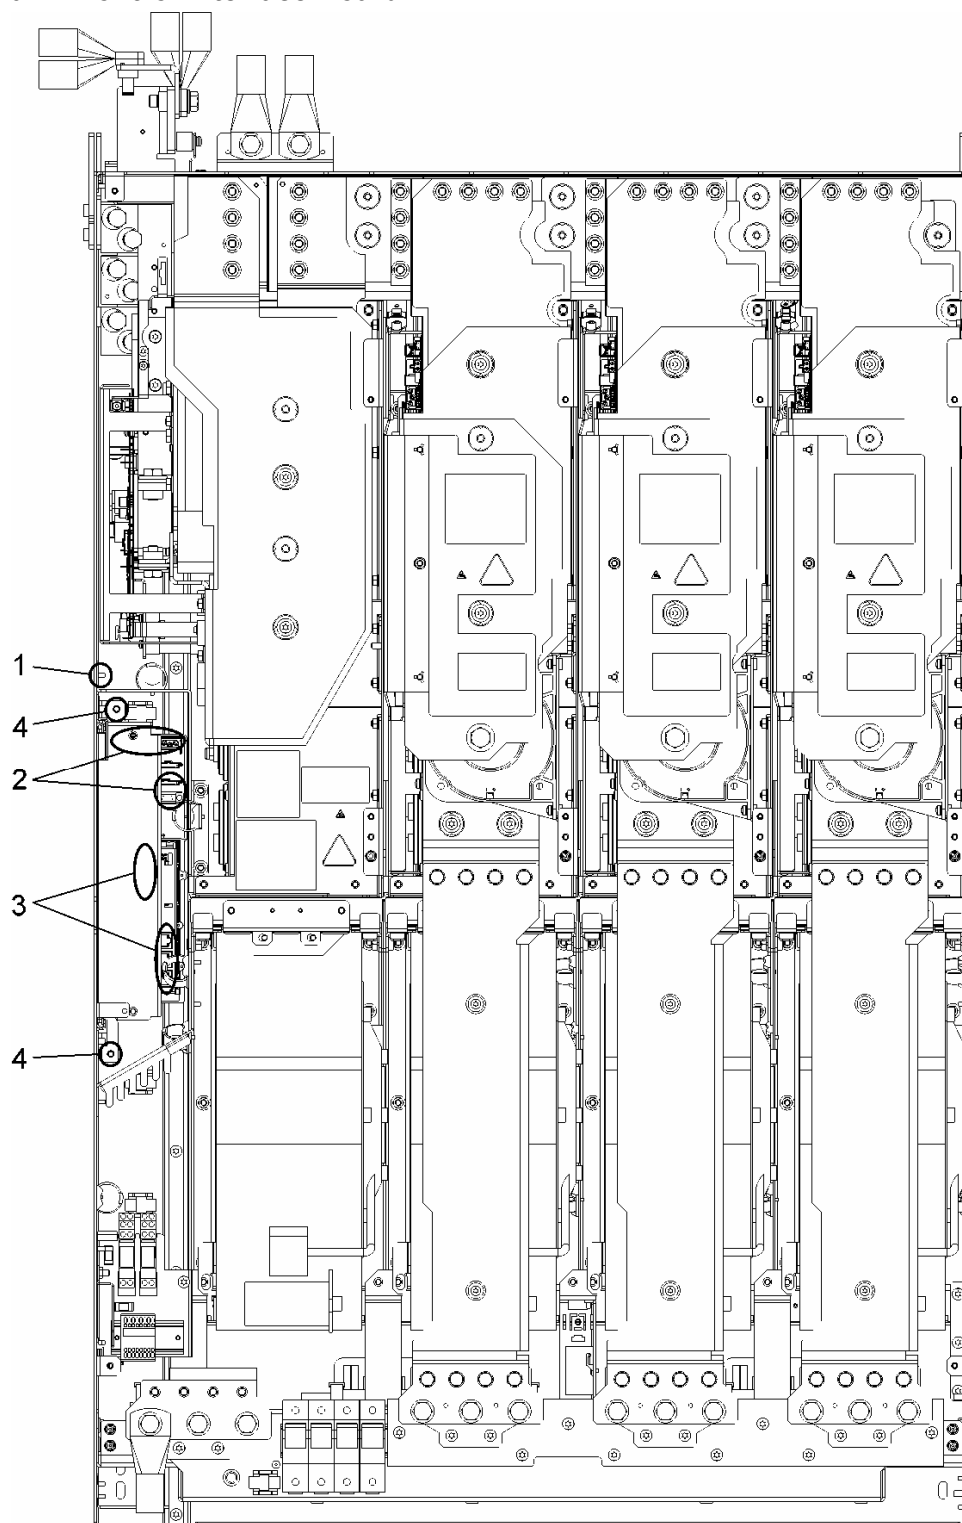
Замена платы Control Interface Board, типоразмер JX
